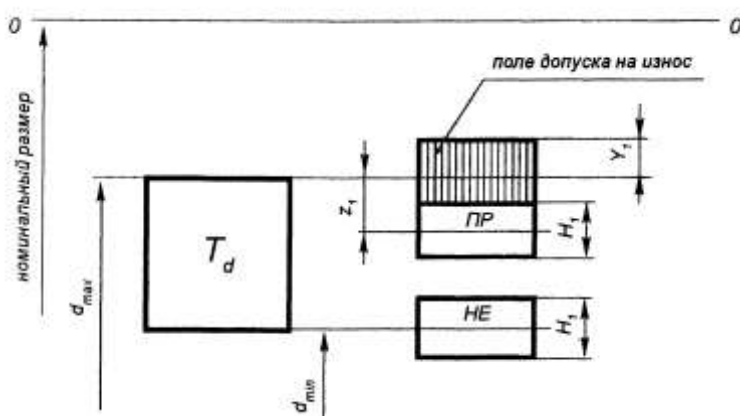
Схема расположения полей допусков калибров для контроля валов изготовленных по квалитетам 6, 7 и 8 при номинальных размерах до 180 мм (для размеров валов изготовленных по квалитетам от 8 до 17, $Y = 0$)
